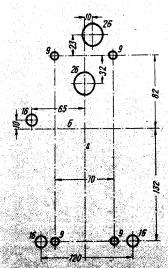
Сверление отверстий для установки на изоляционных пантах контакторов типа КП 504 и КП 514 с задним присоединением
